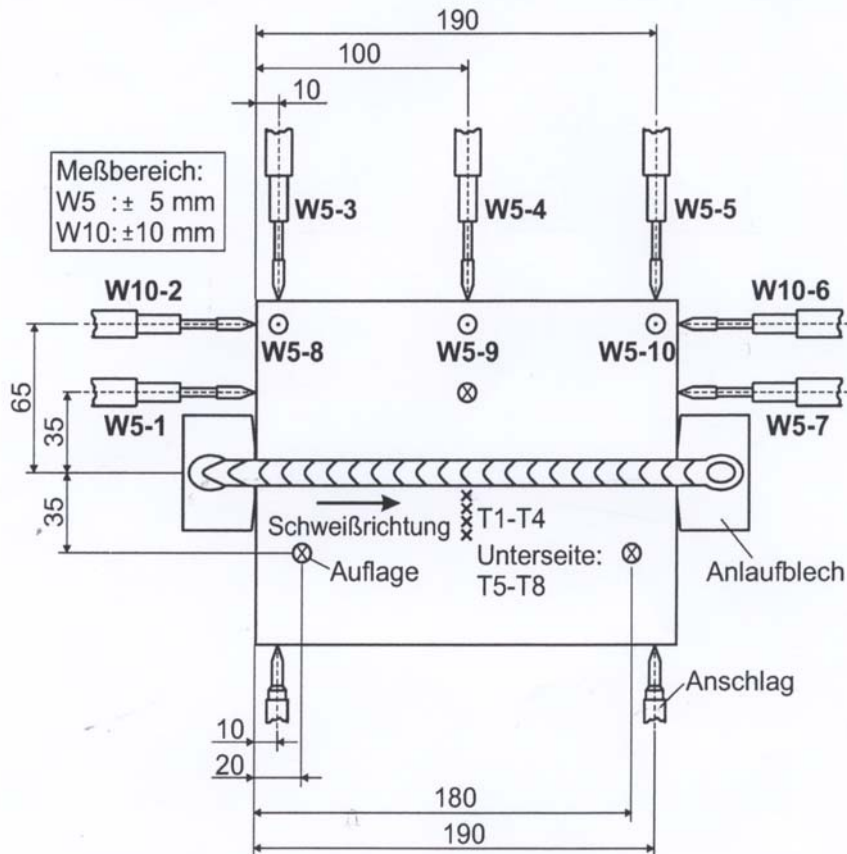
Vermaßung der Schweißprobe (aus [30])
